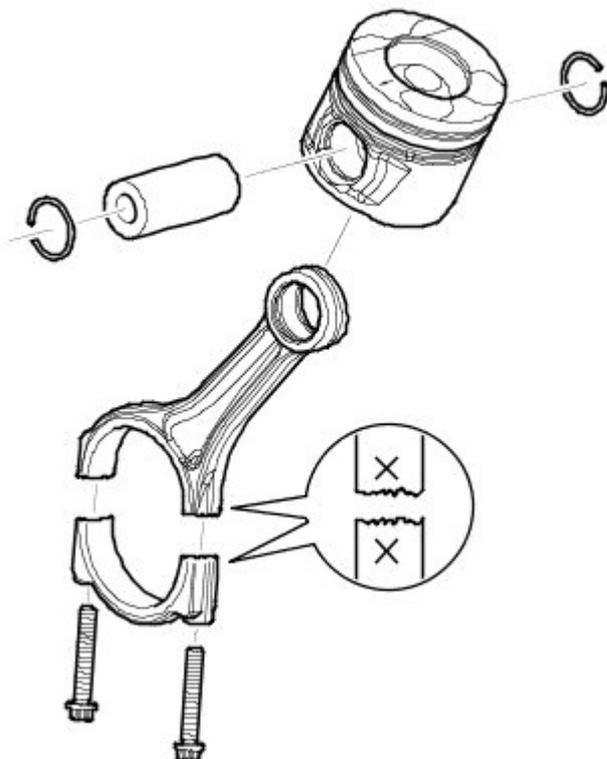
Шатуны и поршни дизельного двигателя 2.7 TD V6
